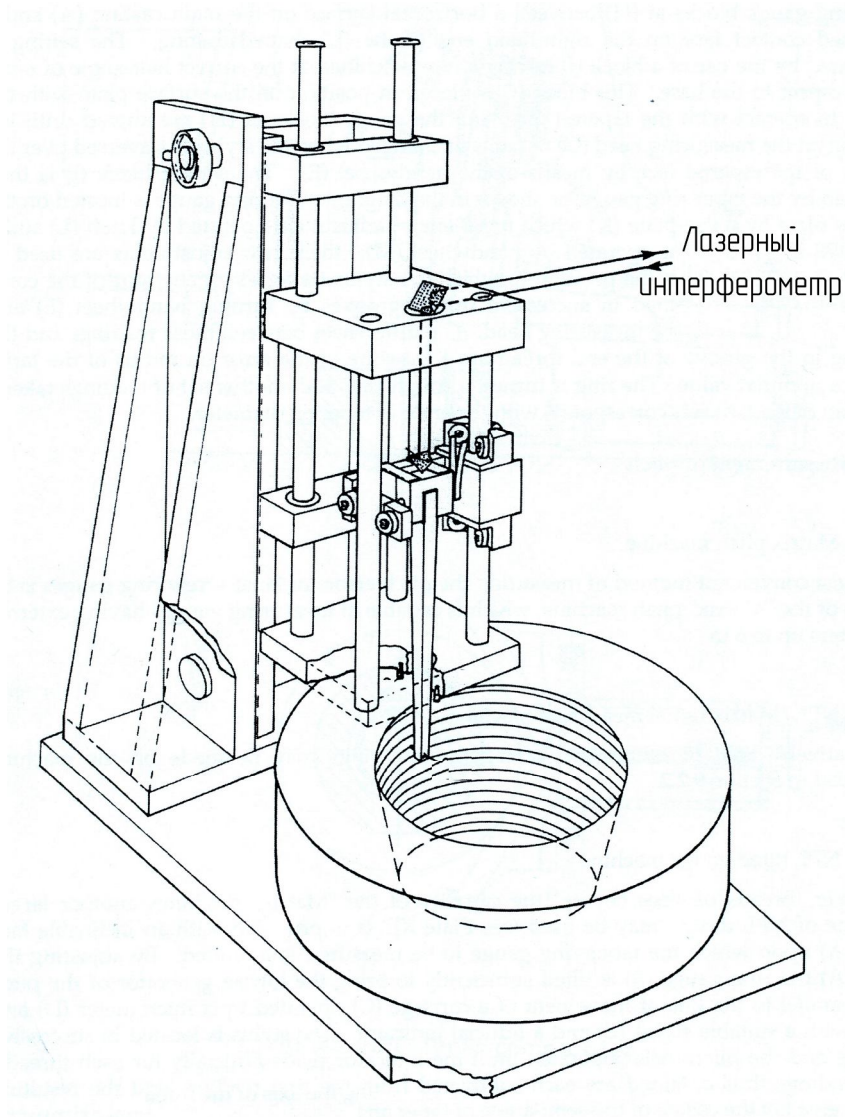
Система для измерения шага резьбовых калибров
